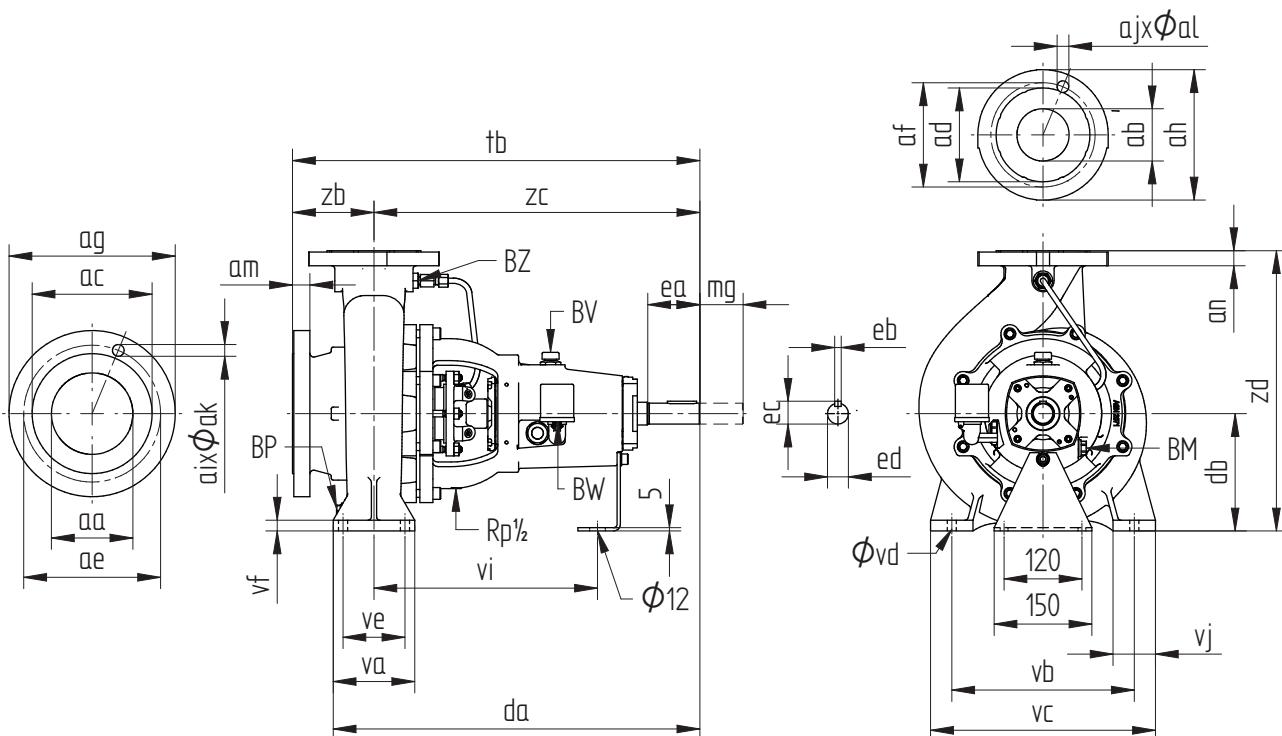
Размеры насоса — группы подшипников 0, 1, 2, 3
